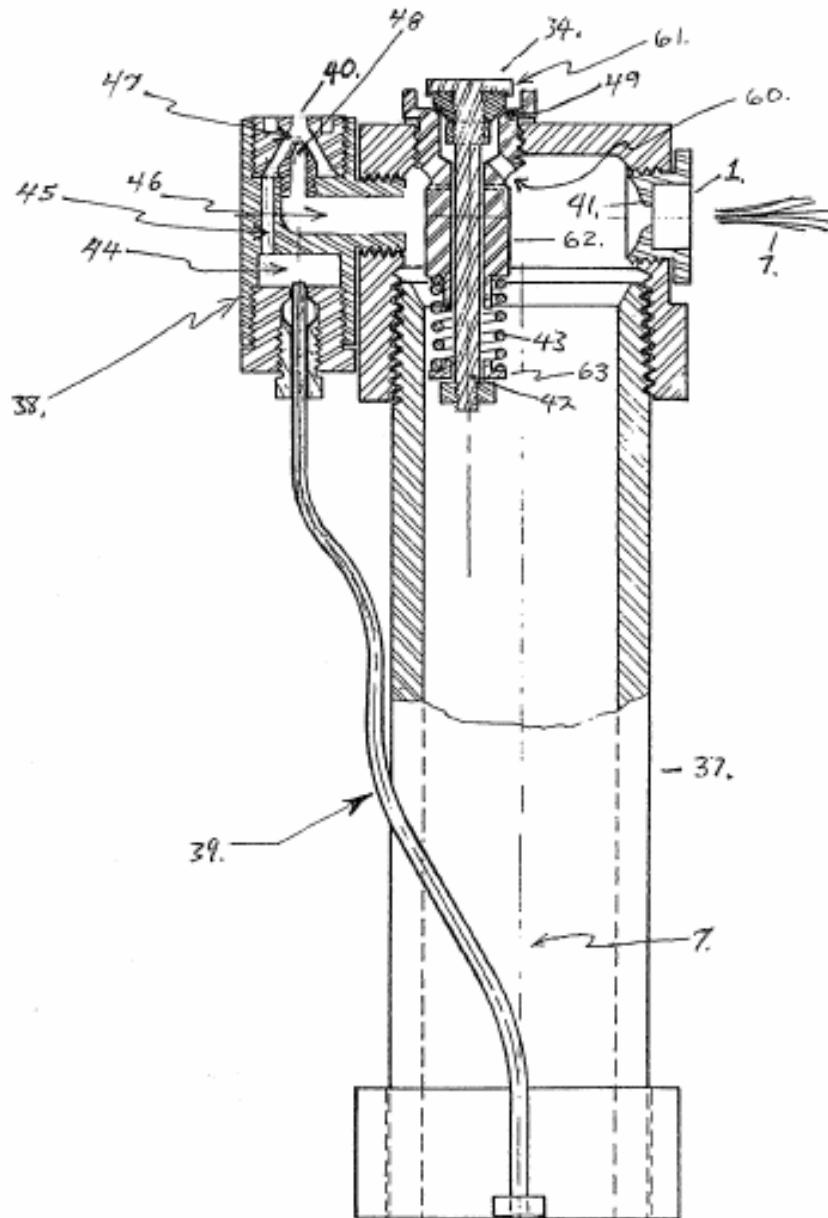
zeigt eine detailliertere Ausführungsform der Speiche 37 mit einem Jet-Siphon-Luftspülmechanismus 38 für Maschinen, die flüssiges Betriebsfluid 7 verwenden. Die Luftleitung 39 verbindet den zentralen inneren Hohlraum der Rotornabe 32 mit dem Einlassbereich 44 des Luftspülmechanismus 38. Wenn sich der Rotor 2 dreht, wird eine kleine Menge Luft, die unvermeidlich in dem Fluid 7 mitgerissen wird, aus dem Fluid 7 zentrifugiert und würde sich ansonsten in der Mitte des Rotors 2 ansammeln, wodurch der zentrifugal induzierte Druckaufbau in dem Arbeitsfluid 7 innerhalb des Rotors 2 verringert wird. Der Jet-Siphon-Spülmechanismus 38 verwendet eine kleine Menge des Fluids 7 unter hohem Druck aus dem Rotor 2 und leitet es über den Durchgang 46 zum Hochdruck-Siphonstrahl 48. Das Fluid 7 wird mit hoher Geschwindigkeit durch den Venturi-Bereich 47 ausgestoßen und angesaugt Luft entlang der Verbindungskanäle 45 durch den Einlassbereich 44 und durch die Luftleitung 39 von der Nabe 32 des Rotors 2. Die Luft, die mit dem Arbeitsfluid 7 im Venturi 47 mitgerissen wird, wird aus dem Auslass 40 des Spülmechanismus entweder radialer oder tangential unterstützender Strahlschub von Schubdüsen 1.
